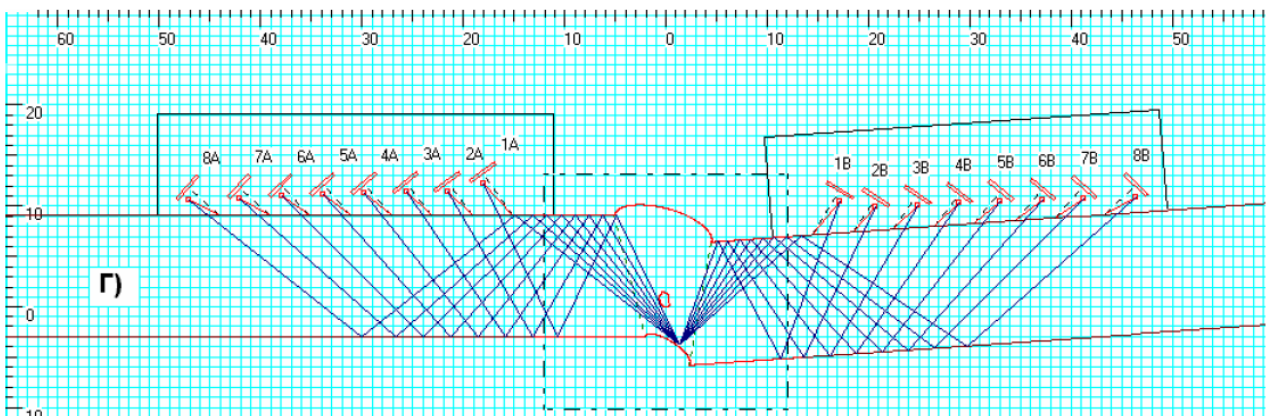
Прозвучивание корня сварного соединения
